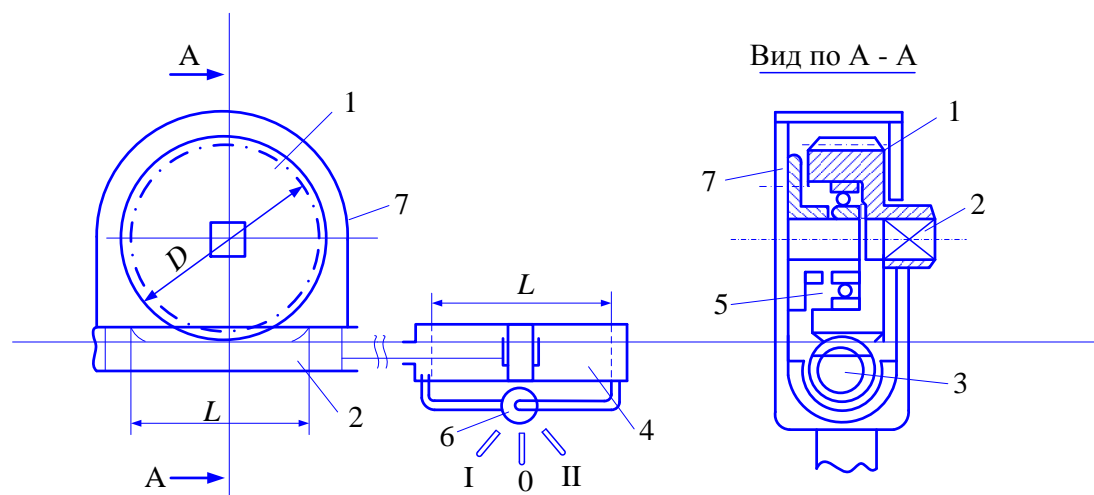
Зубчато-реечный переключатель кранов: 1 – зубчатое колесо ($m=8$, $z=38$), 2 – поворотный квадрат; 3 – зубчатая рейка ($m=8$, $z=10$); 4 – гидроцилиндр ($L=250$ мм); 5 – шариковый подшипник; 6 – гидрораспределитель двухпозиционный; 7 – кожух
